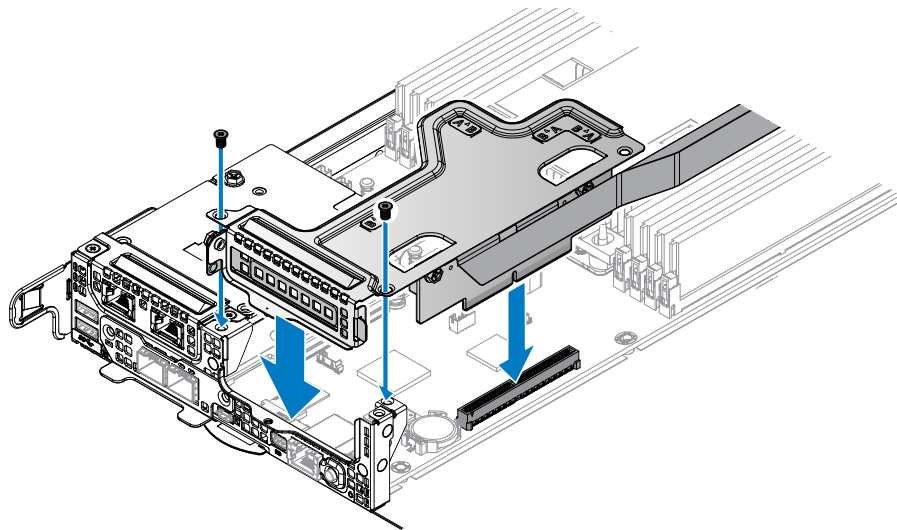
Installation de l'assemblage de carte de montage 3M avant
